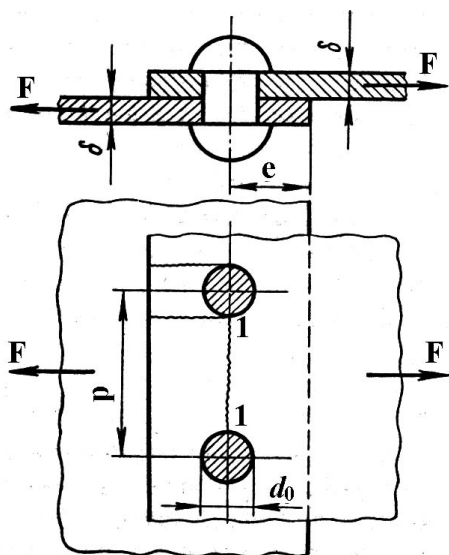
Розрахункова схема заклепкового з'єднання
